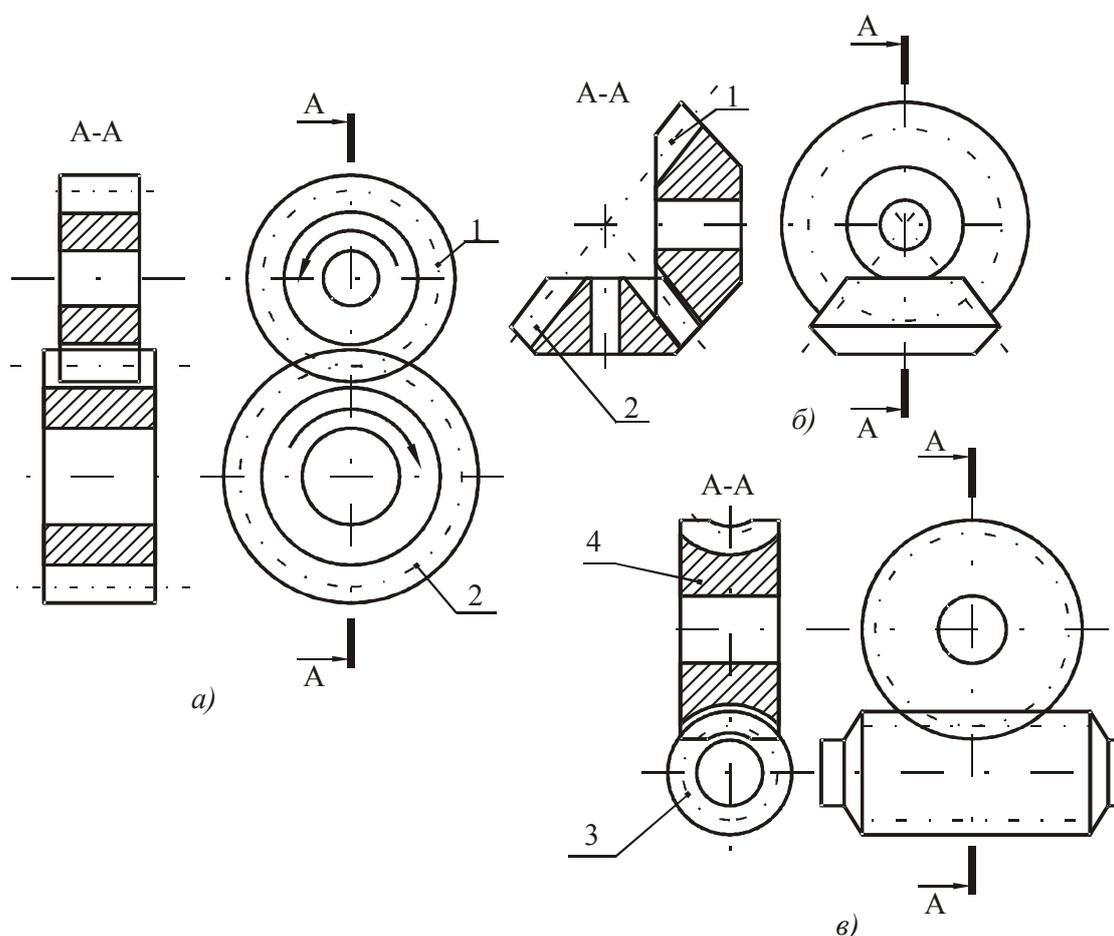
Виды зубчатых передач: *а* – цилиндрическая; *б* – коническая; *в* – червячная; 1 – шестерня; 2 – зубчатое колесо; 3 – червяк; 4 – червячное колесо
